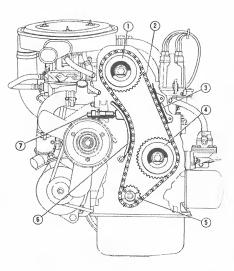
Цепной привод распределительного вала: 1 — ведомая звездочна распределительного вала; 2 — цепь; 3 — услокоитель; 4 — ведомая звездочка промежуточного вала; 5 — ведущая звездочка; 6 — натяжное устройство; 7 — плунжер.
